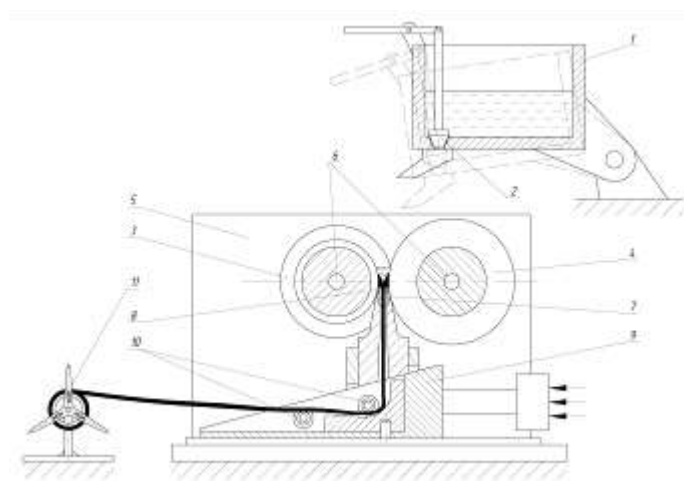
Устройство для непрерывного литья, прокатки, прессования по патенту № 73245:
